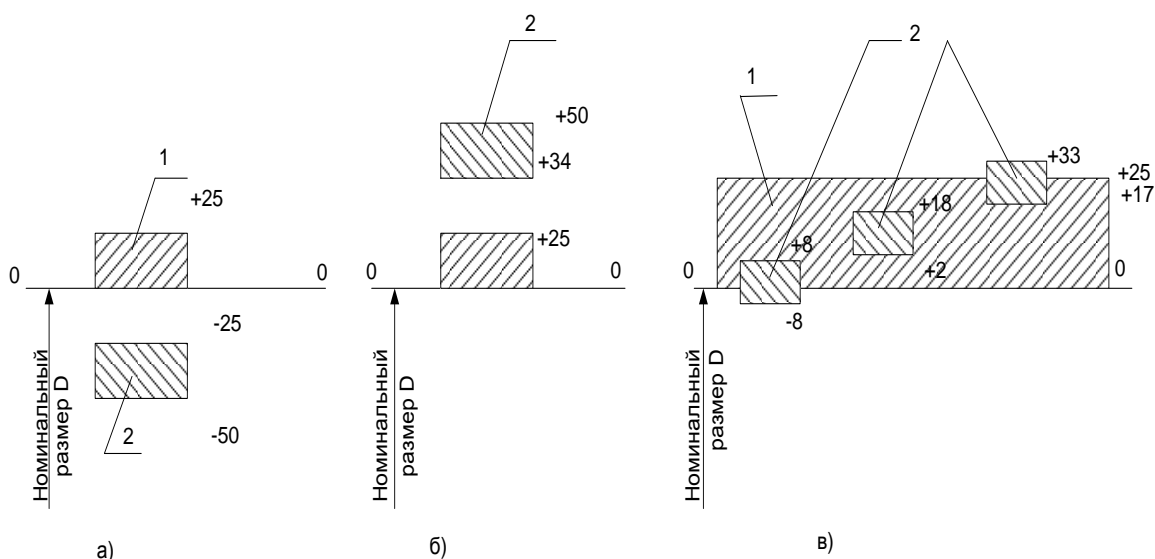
Поля допусков: отверстия-1 вала- 2.
